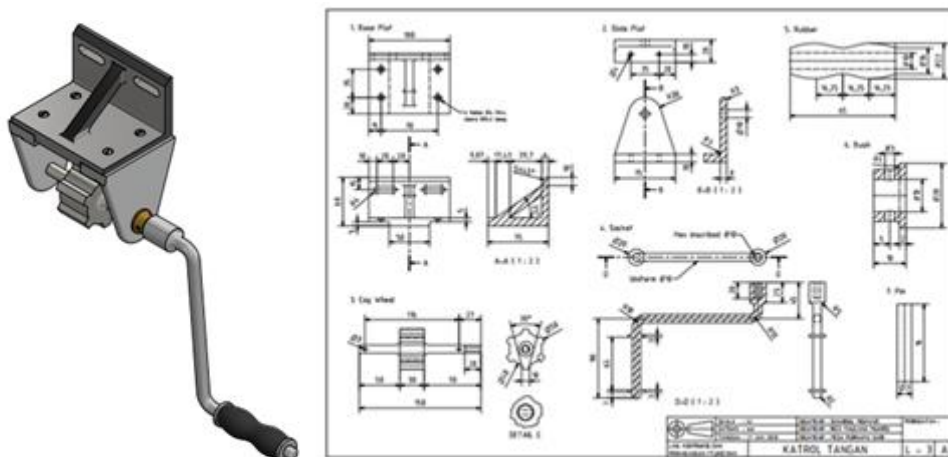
Cara kerja (*shop drawing, layout drawing*)
